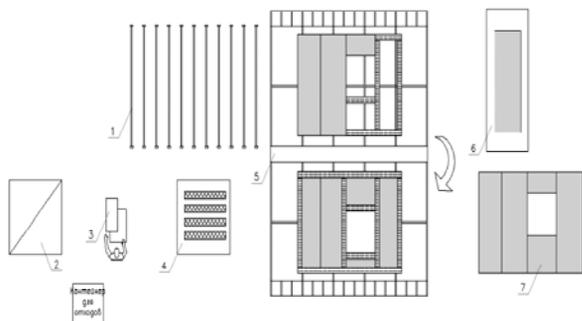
Схема участка укладки утеплителя и обшивки каркаса панели: 1 – ригельная станция; 2 – подстоечное место для утеплителя; 3 – станок ленточный вертикальный BS 600; 4 – подстоечное место для теплоизоляционных плит; 5 – поворотный стол ВТ-8; 6 – подстоечное место для облицовочных панелей; 7 – готовая стеновая панель.
